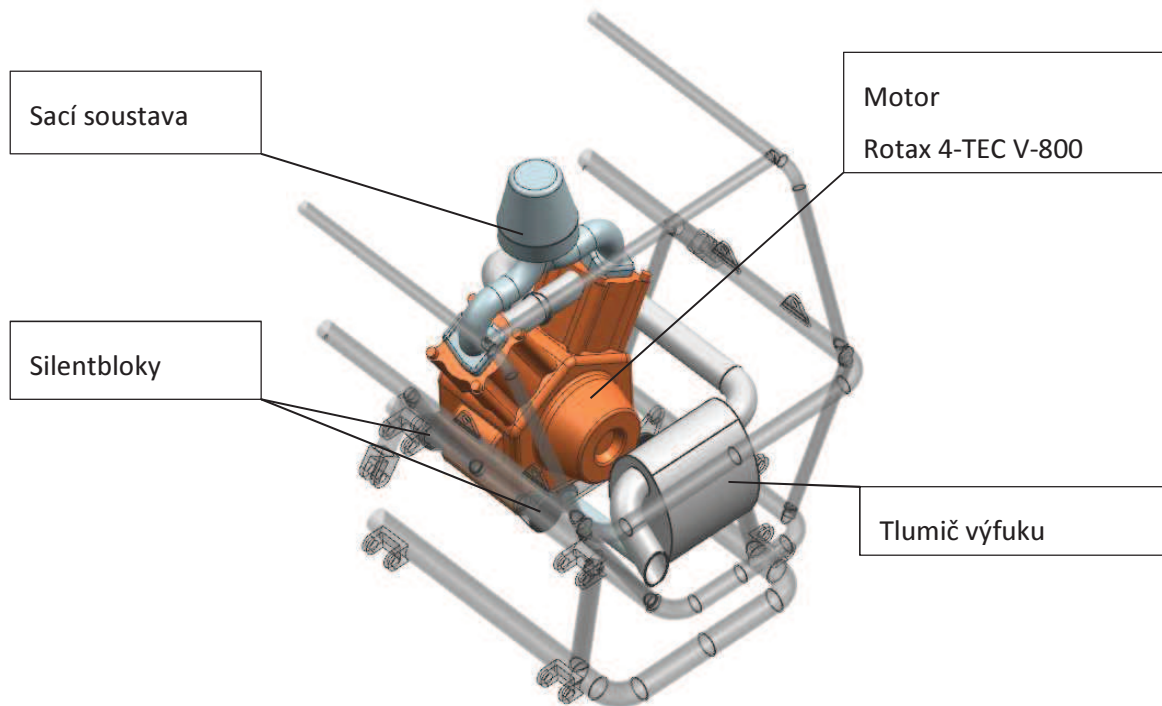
Motor Rotax 4-TEC V-800 [26]
